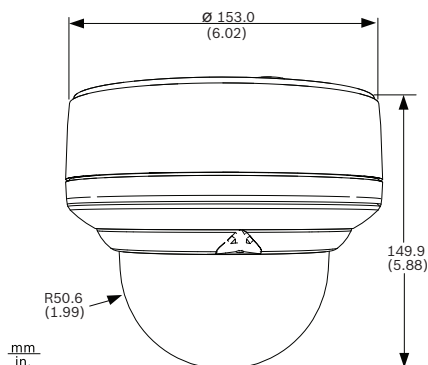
Dimensões do suporte para montagem saliente para interior
